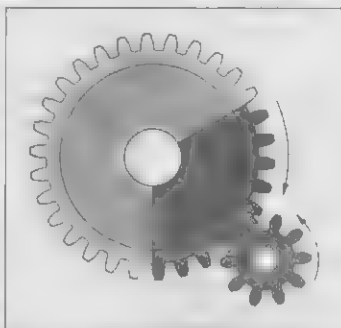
Передаточное число 3:1. Шестерня с 10 зубьями сделала полный оборот, а шестерня с 30 зубьями прошла только треть пути.
